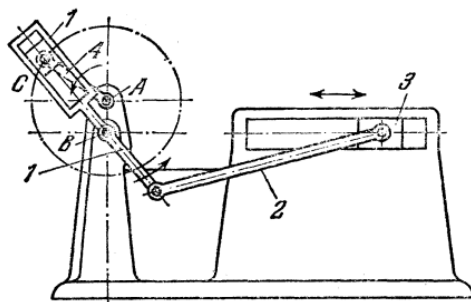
Кулисно-рычажный шестизвенный механизм с прицепным шатуном и ползуном
